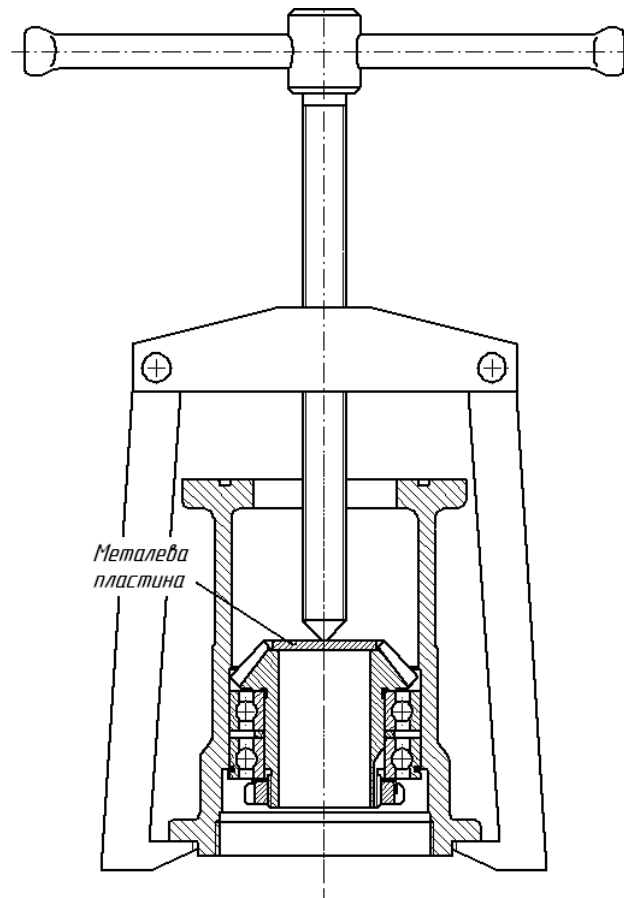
Проводиться видалення шестерні веденої та підшипників із корпуса редуктора кутового шляхом випресування.
